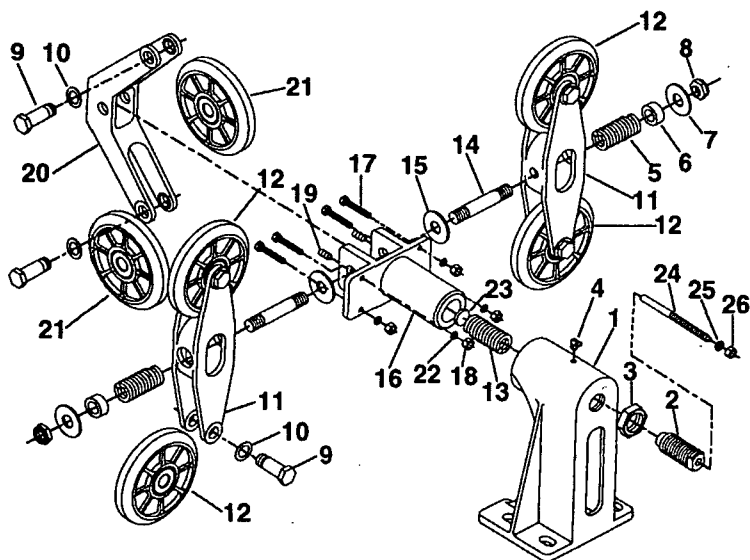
Разобранный роликовый башмак Model A (ELSCO): 1 – кронштейн, 2 – регулировочный винт ступицы, 3 – регулировочная гайка ступицы, 4 – пресс-масленка, 5 – пружина бокового рычага, 6 – фибровая втулка, 7 – плоская шайба; 8 – стопорная гайка, 9 – палец колеса; 10 – стопорная шайба пальца колеса, 11 – боковой рычаг, 12 – неопределенное колесо, 13 – пружина ступицы, 14 – палец бокового рычага, 15 – резиновая шайба, 16 – ступица, 17 – регулировочный винт бокового рычага, 18 – шестигранная гайка, 19 – установочный винт, 20 – торцевой рычаг, 21 – неопределенное колесо, 22 – стопорная шайба, 23 – шайба опорная, 24 – регулировочный винт, 25 – стопорная шайба, 26 – гайка
